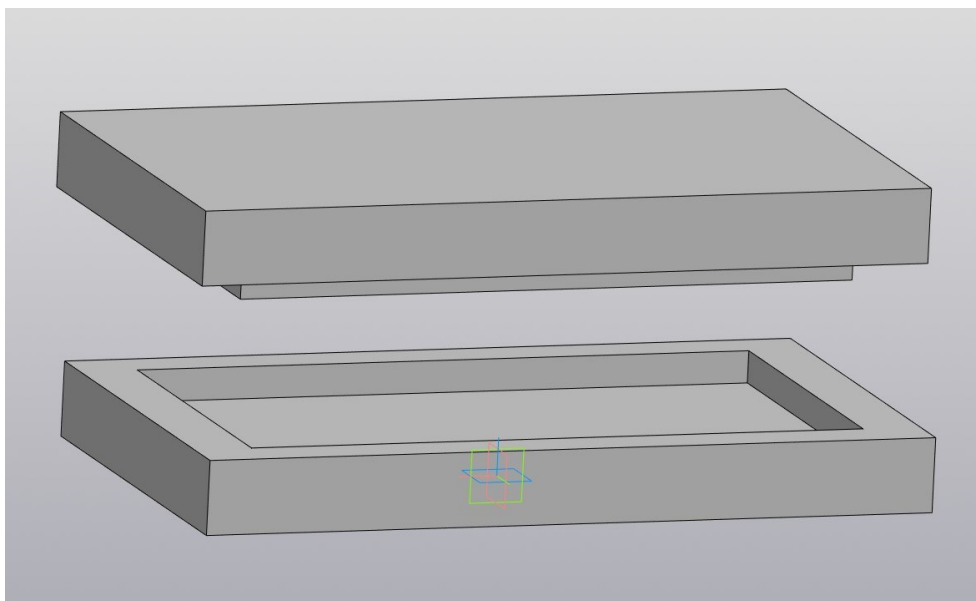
3D модель прес – форми для формування нижньої панелі корпусу платформи.
